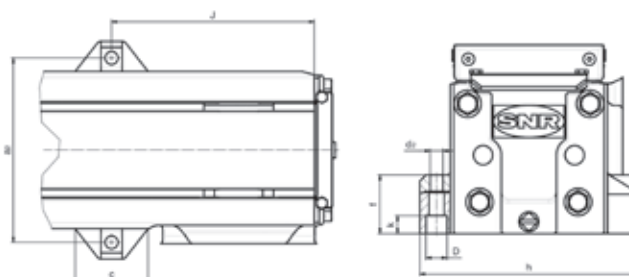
Abmessungen Befestigungselement AXF
